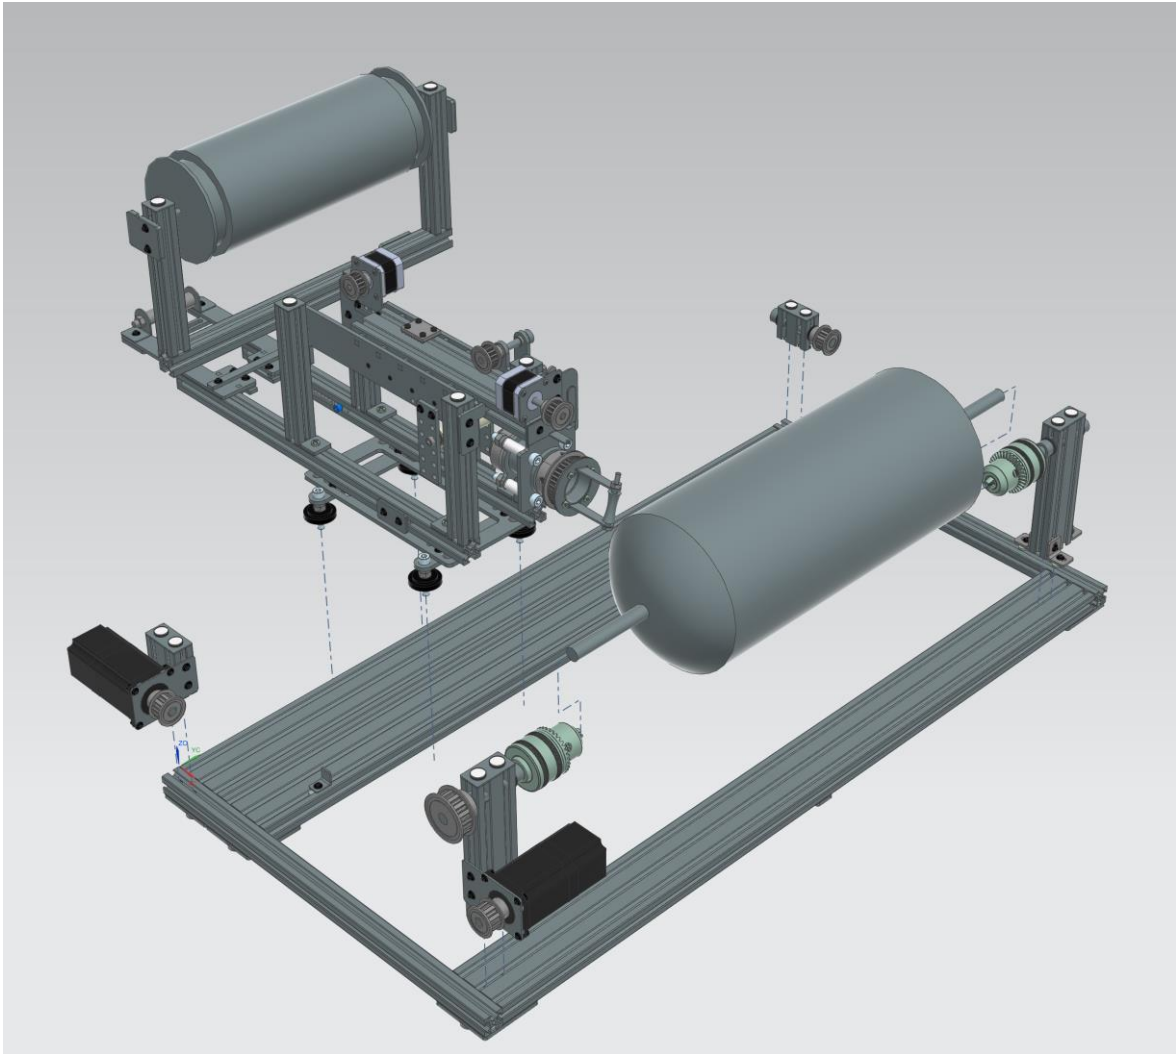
Rappresentazione, in vista isometrica, del modello CAD dell'assemblaggio tra: barre posteriori, base e telaio del carro, Traslazione della testa di deposizione, Rotazione della testa di deposizione e Percorso del towpreg
